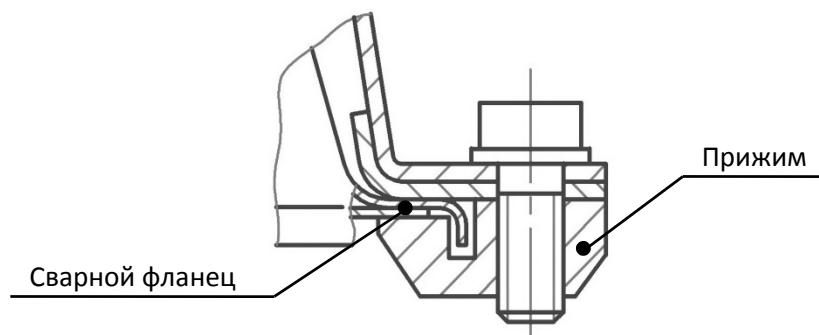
Закрепление надстроек с использованием сварных фланцев.
